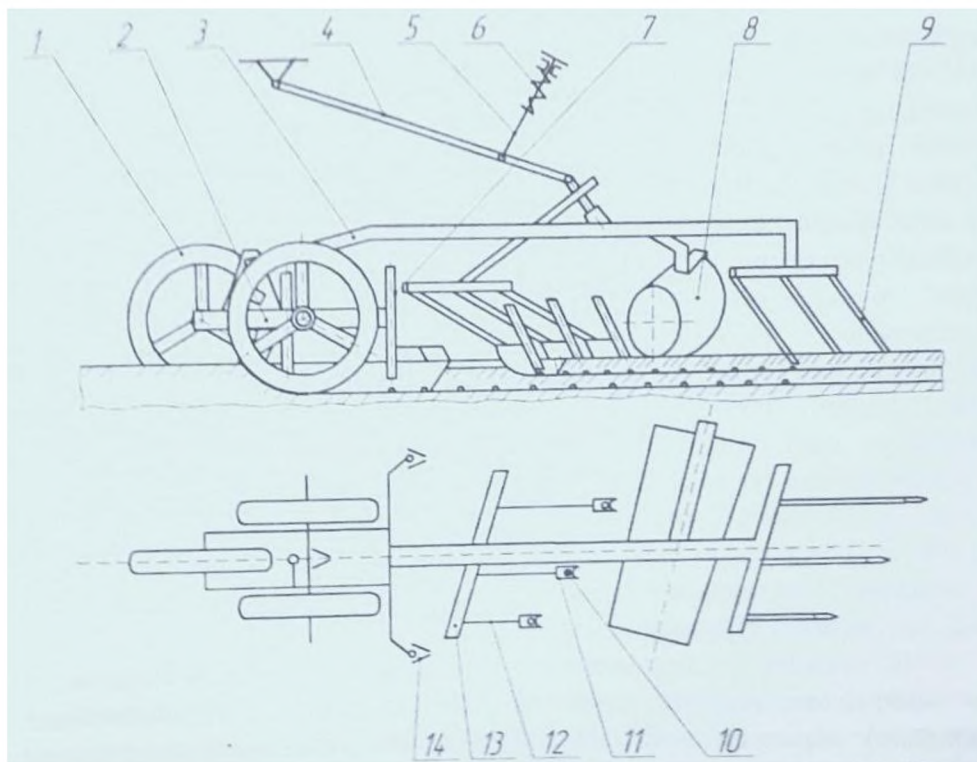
Схема ґрунтообробно-посівної конструкції М.С. Шведика [7]: 1 – кільчатий коток; 2 – рамка; 3 – штаба; 4 – повідець; 5 - натискна штанга; 6 – пружина; 7 – тукопровід; 8 – конічний коток; 9 – зубовий загортач; 10 – насіннепровід; 11 – кілевидний сошник; 12 – повідець; 13 – траверса; 14 – загортач
